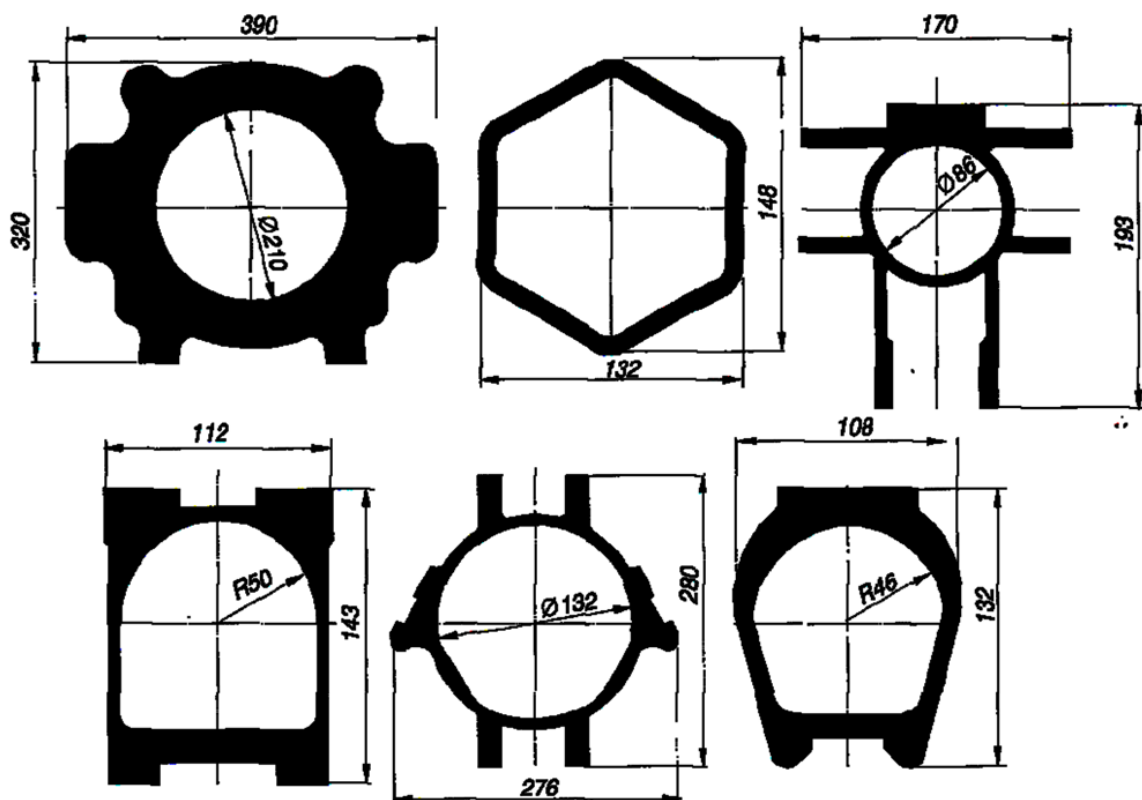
Полые профили больших типоразмеров, полученные прессованием.
